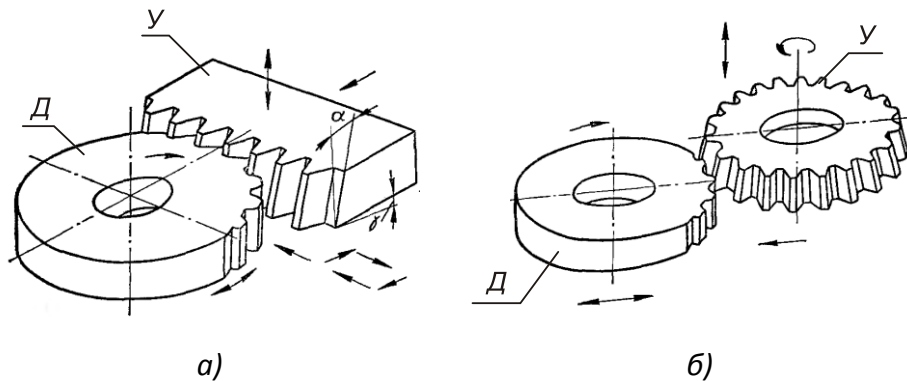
Оброблення зубчастих деталей гребінками і довбачами
